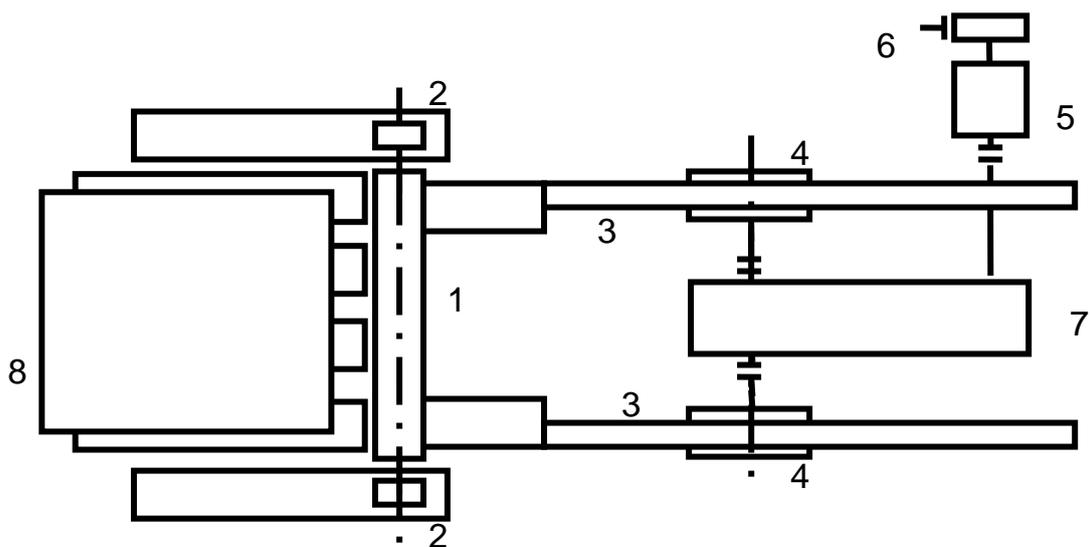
Кинематическая схема сталкивателя слябов:
